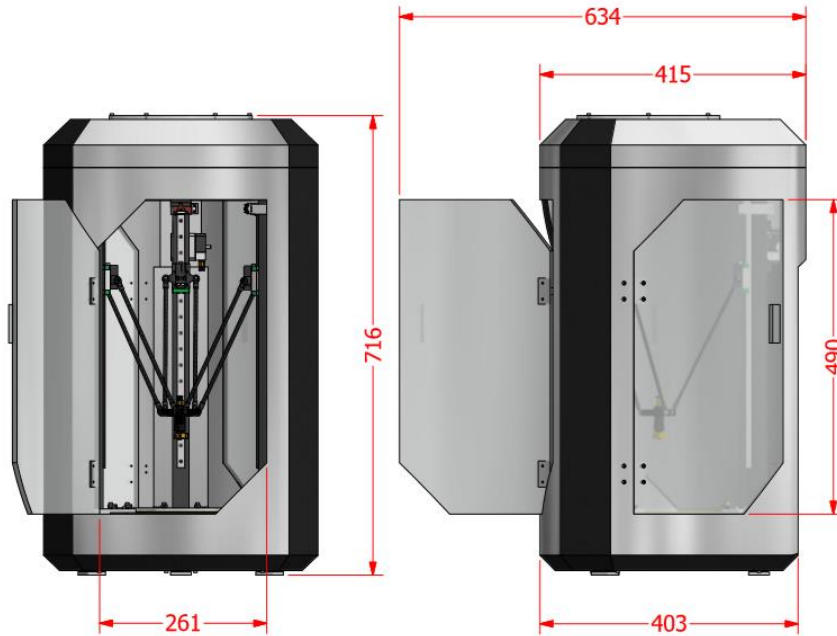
Dimensiones generales de la impresora (en milímetros).
